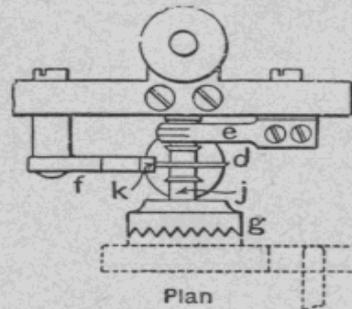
et 96. — Cohéreur en élévation et en plan.
